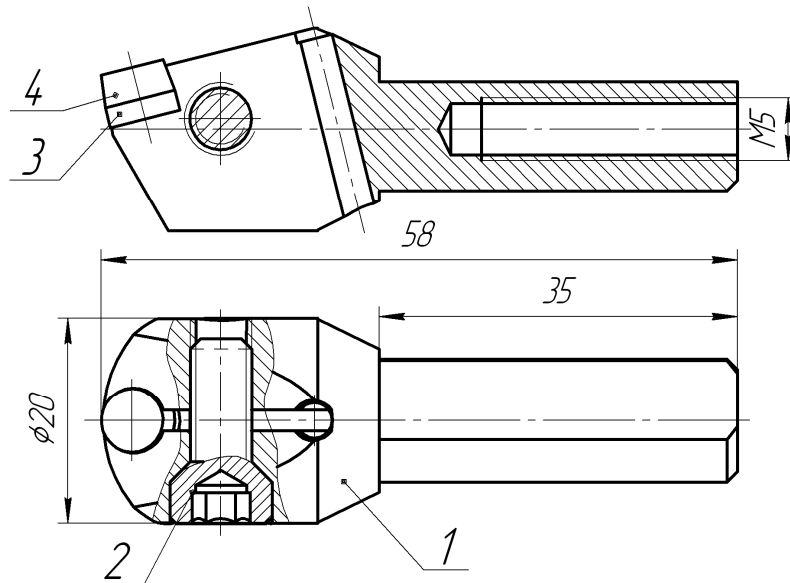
Новий вузол закріплення круглої пластинки з НТМ:
